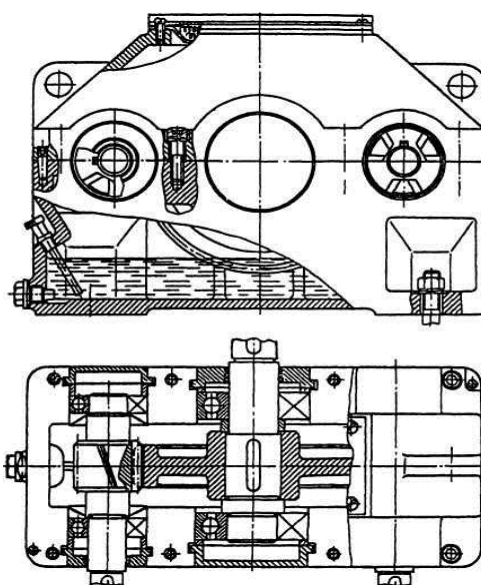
Цилиндрический одноступенчатый зубчатый горизонтальный двухпоточный редуктор с двумя быстроходными валами
